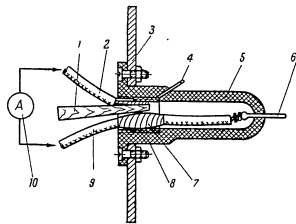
Способ подключения амперметра в гнездо корпуса предохранителя:
